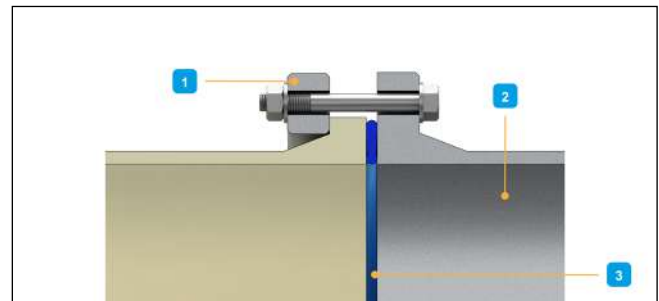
Flange solta em PRFV com anel de retenção em aço utilizando uma junta flangeada perfil tipo anel
